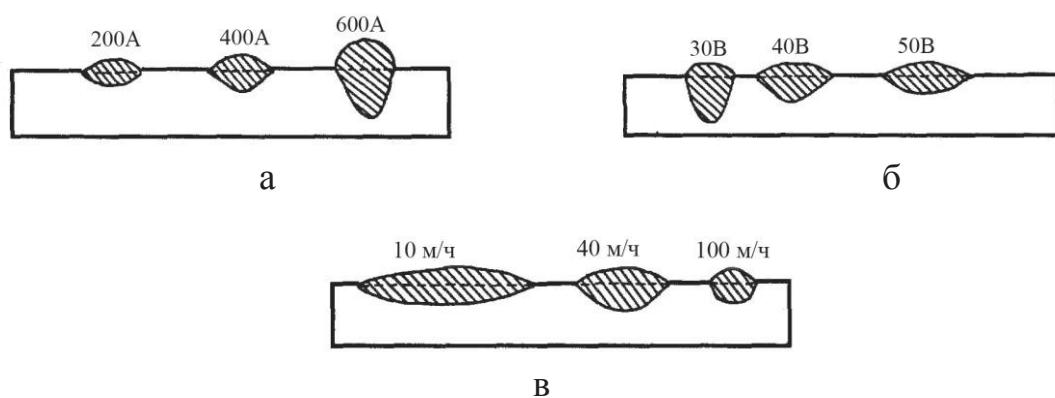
Влияние параметров режима на форму шва: а – варочный ток; б – напряжение дуги; в – скорость сварки
